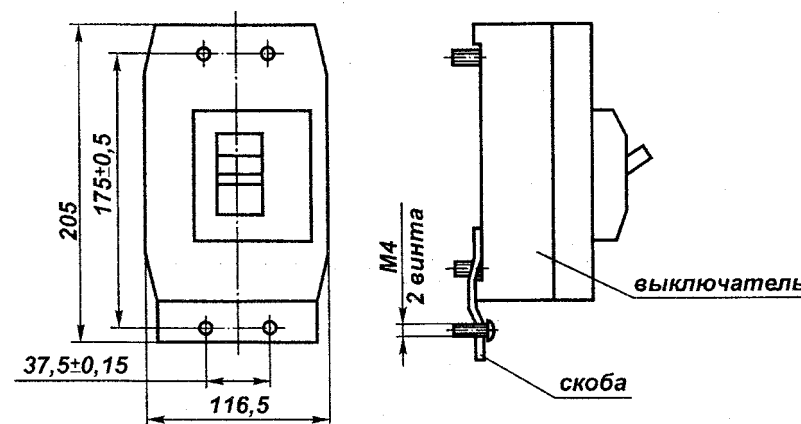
Установочные размеры выключателей для крепления на рейках с закрытым пазом.
